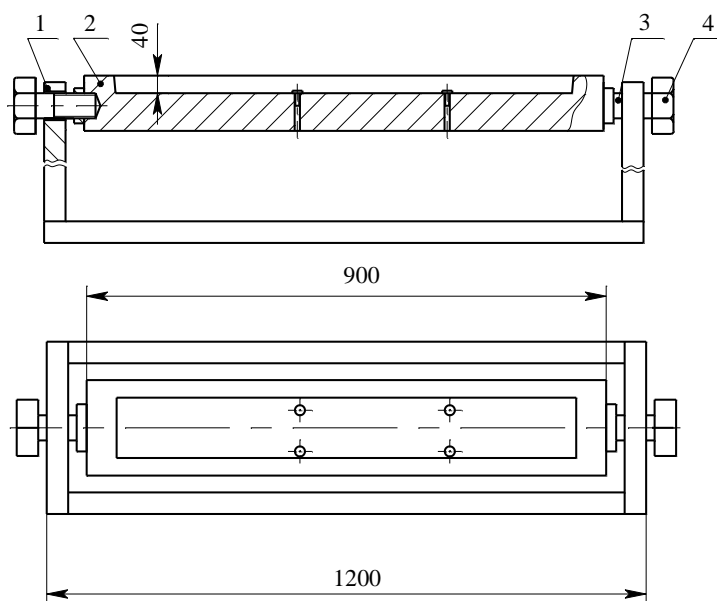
Кокиль вытряхной для отливки внутреннего холодильника (схема):
